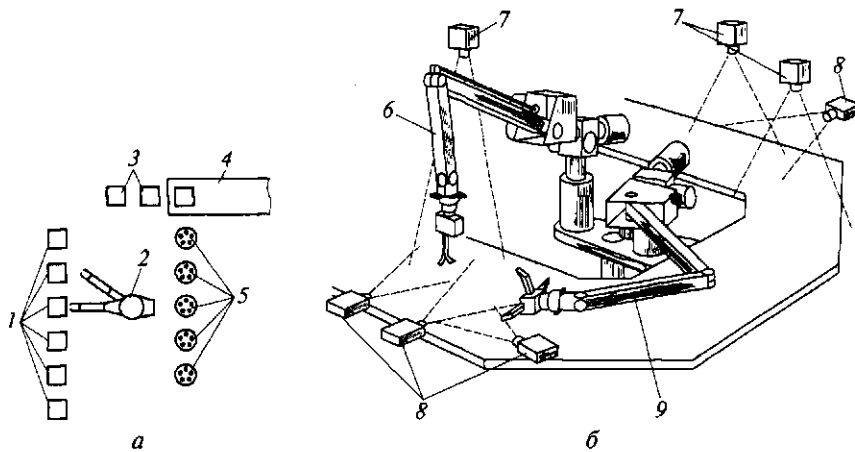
Компонновка сборочного РТК (а) и его рабочая зона (б):
